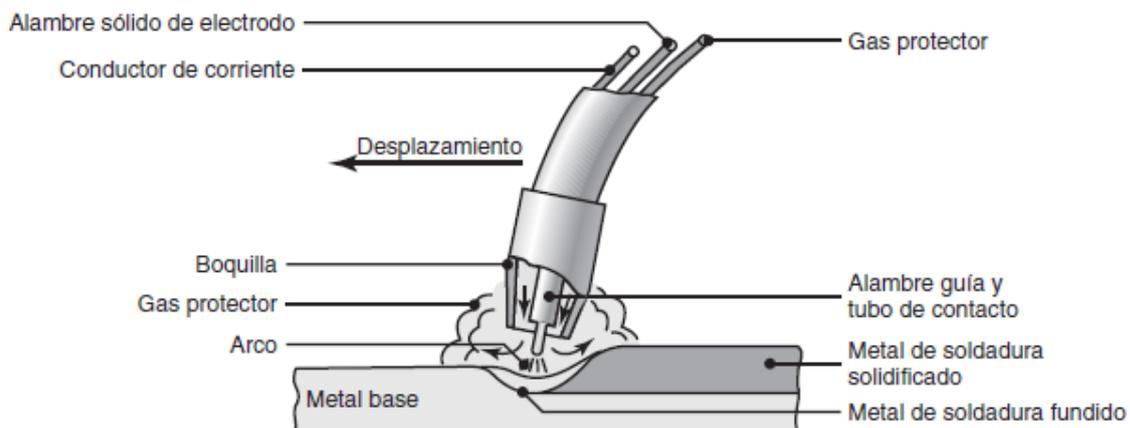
Soldadura por arco metálico y gas (Fuente: *Manufactura, Ingeniería y Tecnología*)
